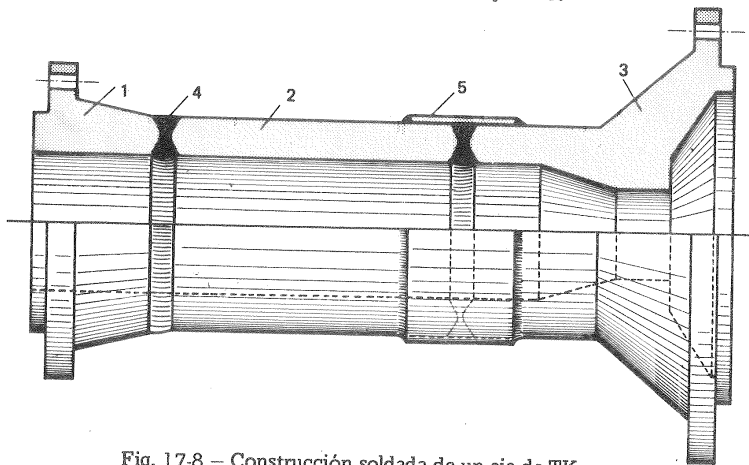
Construcción soldada de un eje de TK
